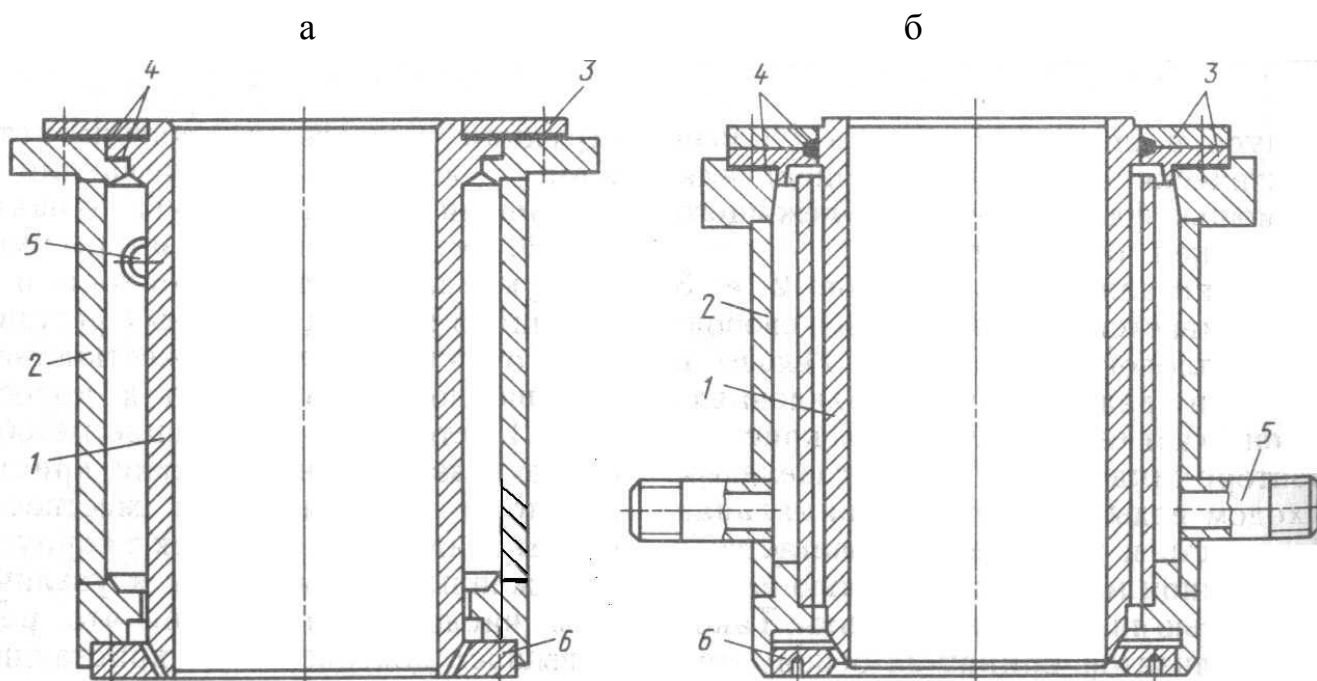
Схема однокамерного (а) и двухкамерного (б) кристаллизаторов скольжения: 1 – гильза; 2 – корпус; 3 – верхний фланец; 4 – прокладки; 5 – патрубок; 6 – нижний фланец
